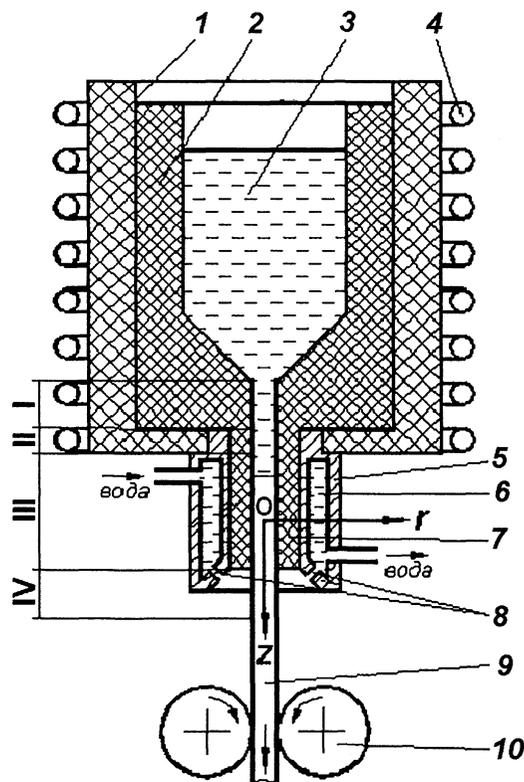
Схема установки непрерывного вертикального литья: 1 – футеровка; 2 – тигель; 3 – расплав; 4 – индуктор; 5 – металлический корпус кристаллизатора; 6 – вода; 7 – рабочая втулка кристаллизатора; 8 – отверстия для вторичного охлаждения; 9 – отливка; 10 – вытягивающее устройство
